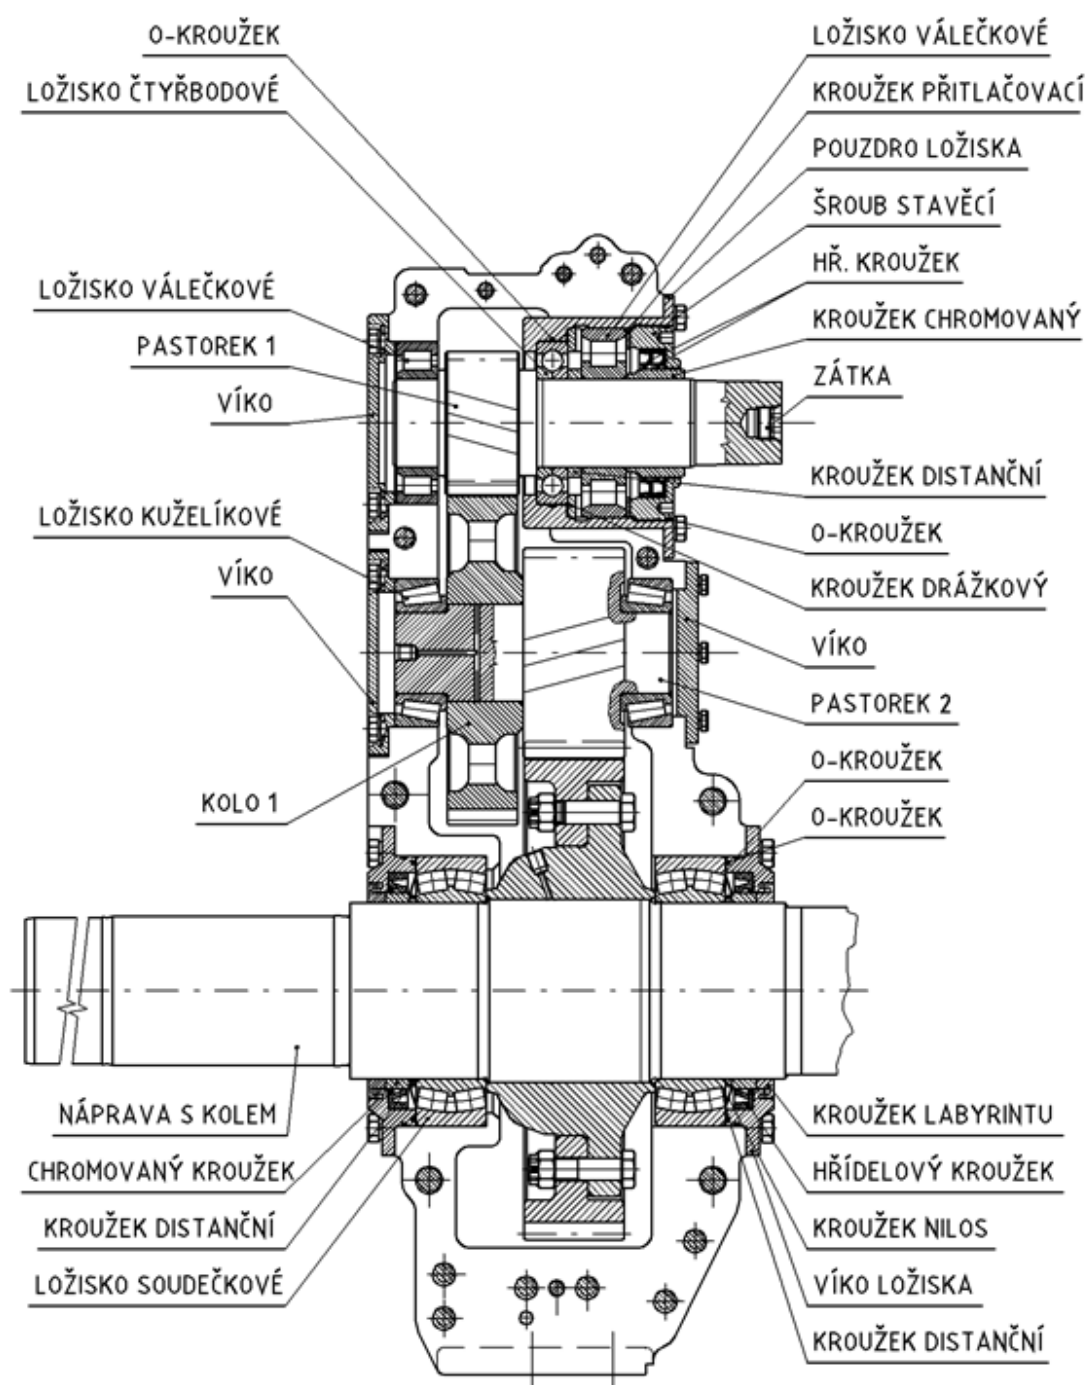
Řez zubovou spojkou KWD – ZK 110-2 [5]
